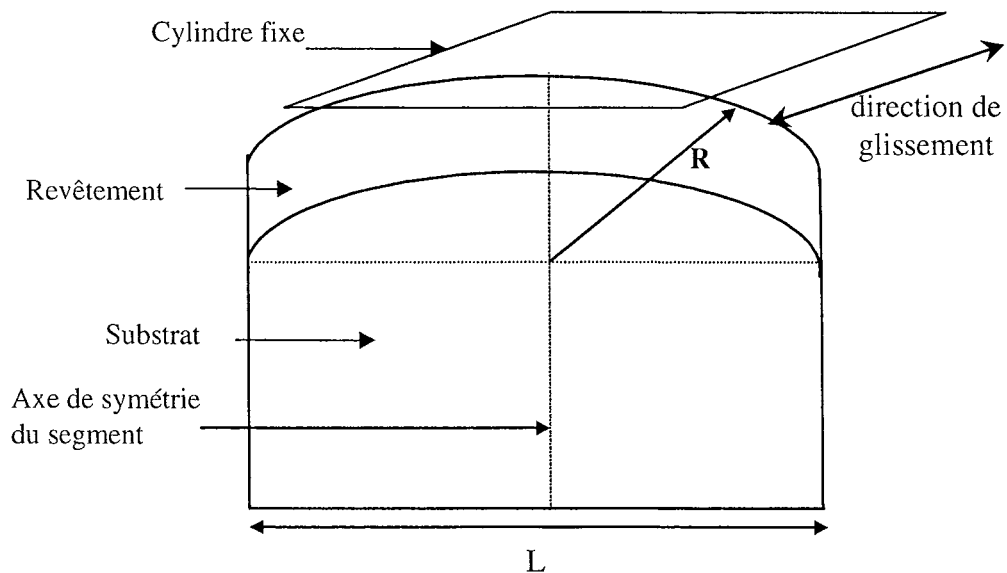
Géométrie du contact entre le segment et le cylindre.
